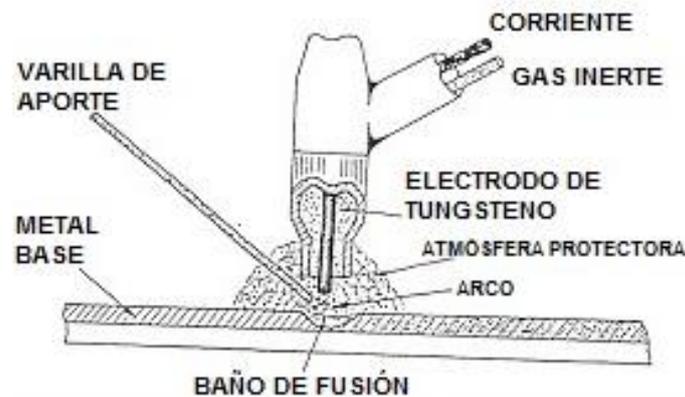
Elementos del proceso de soldadura TIG
